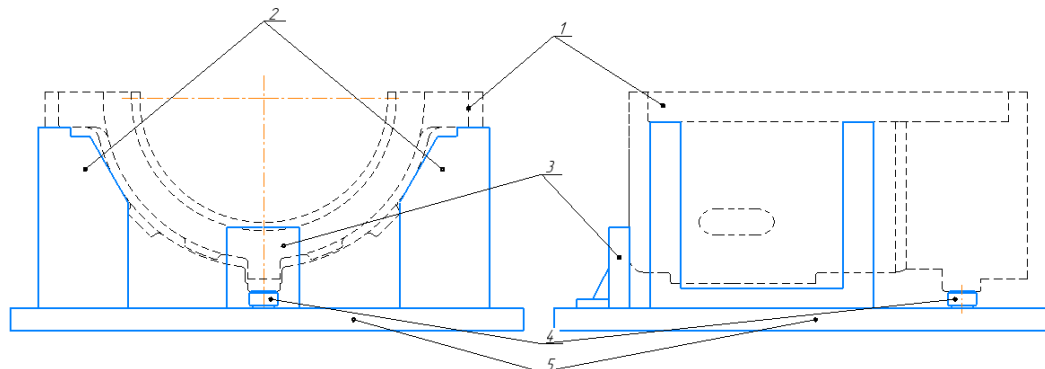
Схема закрепления с использованием вспомогательного оборудования
